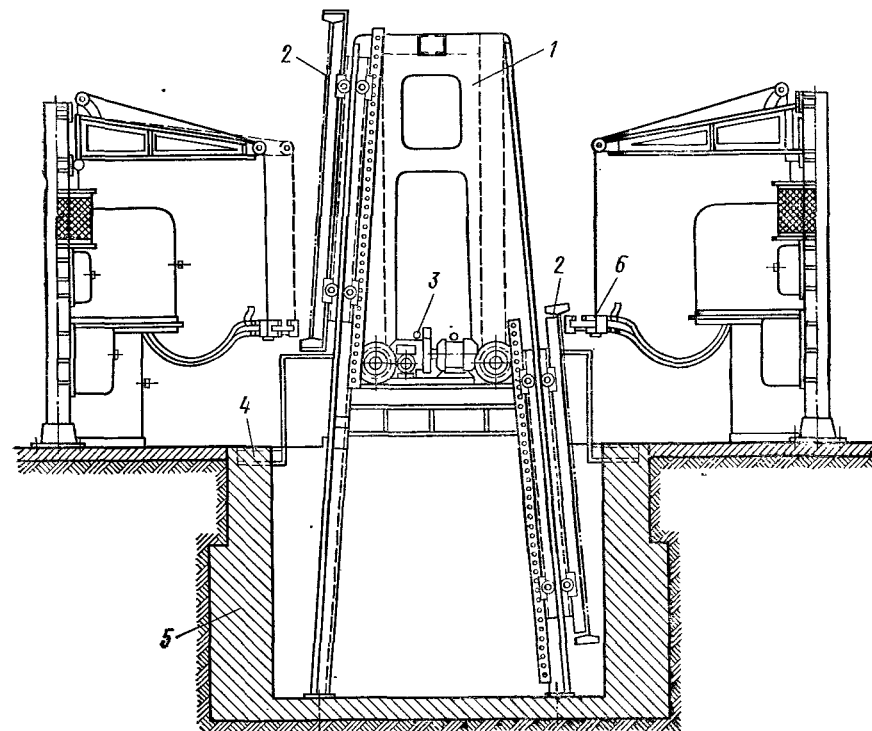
Манипулятор для сборки и сварки арматурных пространственных каркасов:
